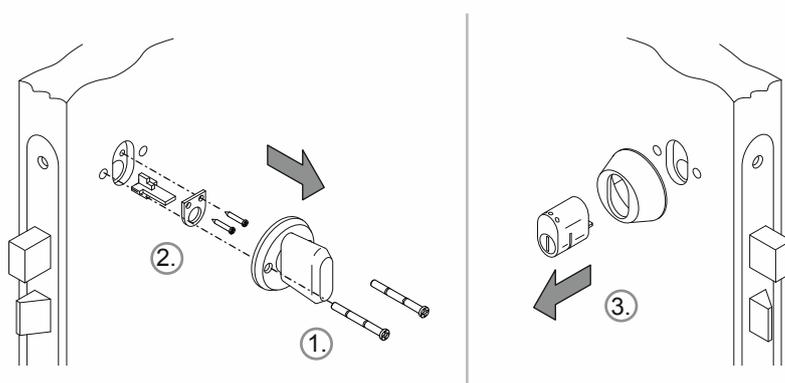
Демонтаж старого цилиндра: скандинавский овальный профиль
